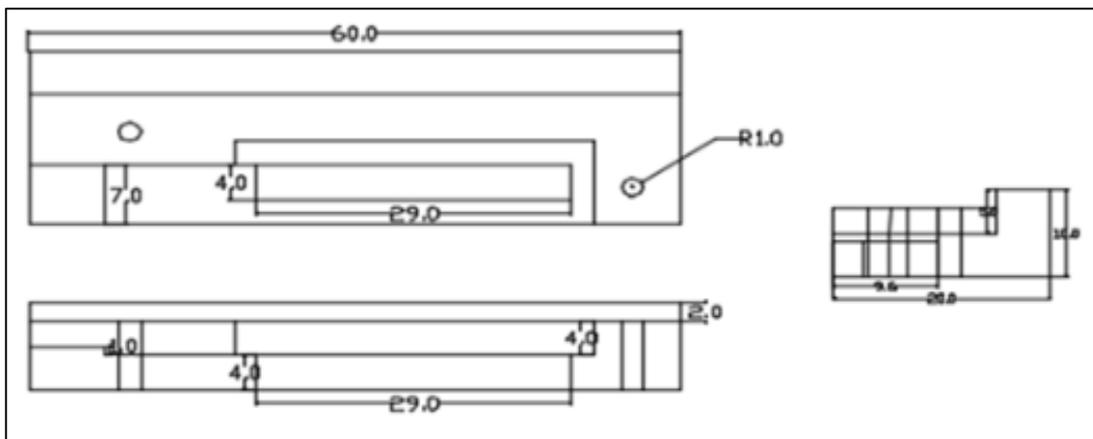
Desenho em CAD do suporte periférico na placa para cabo flat.
